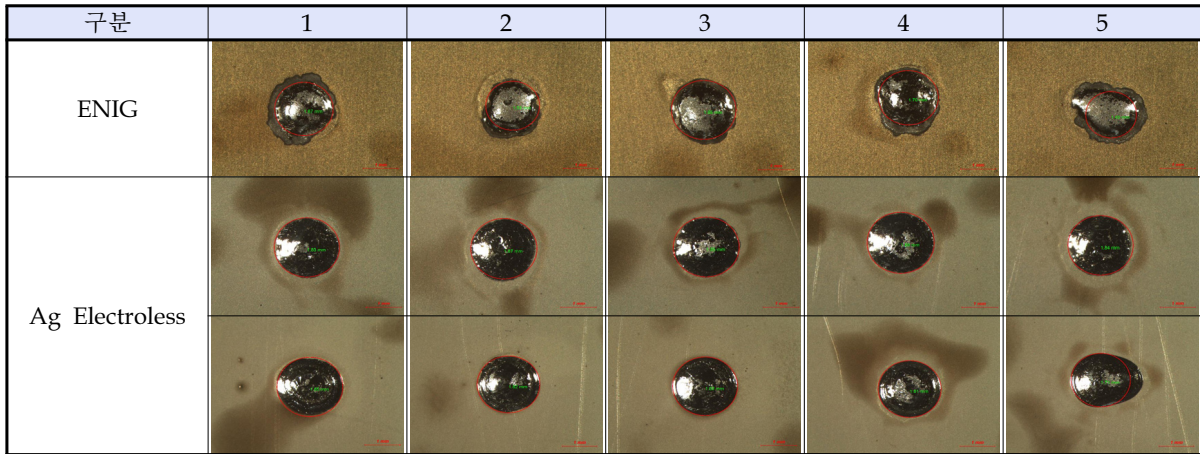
Ag Electroless layer 상의 Solder Ball Wettability.
